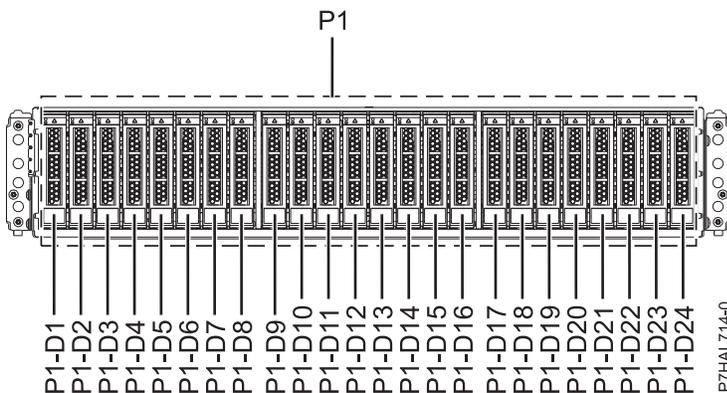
Vorderansicht des Plattenlaufwerkgehäuses 5887 mit den Positionen der Plattenlaufwerke
